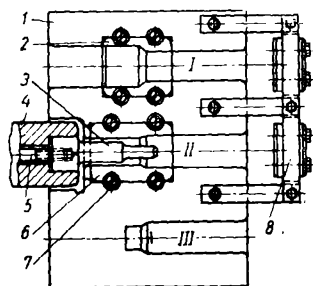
Высадочный штамп для обжатия концов труб: 1 — блок матриц; 2 — вставка правочная; 3 — пуансон; 4 — державка; 5 — винт; 6 — вставка формовочная; 7 — винт крепления вставок; 8 — упор-планка
